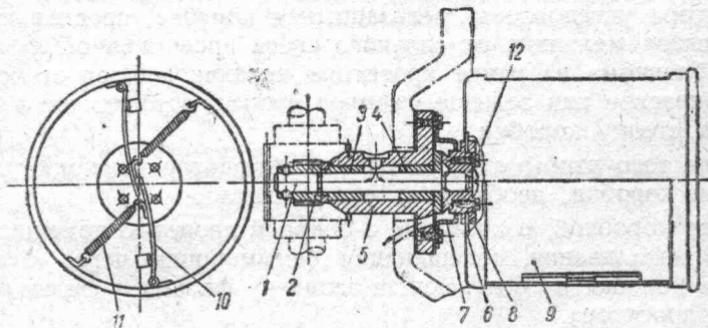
Обтюраторный механизм в разрезе: 1 — вал; 2 — малая шестерня; 3, 4 — втулки; 5 — подшипник; 6 — фланец; 7 — колпачок; 8 — шайба; 9 — обтюратор; 10 — заслонка; 11 — пружины; 12 — винты
